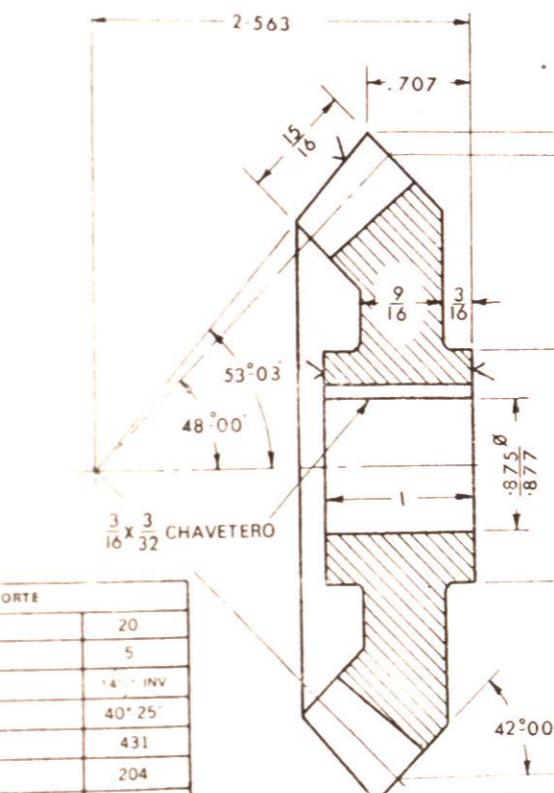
Dibujo de taller de un engranaje cóncavo.
